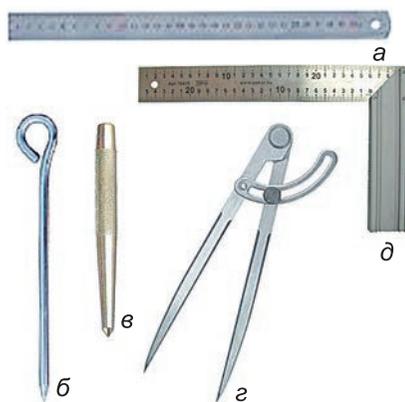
Разметочные слесарные инструменты: а – масштабная линейка; б – чертилка; в – кернер; з – слесарный циркуль; д – слесарный угольник
